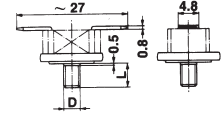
Flachstecker 4.8 x 0.8 seitlich abgewinkelt
